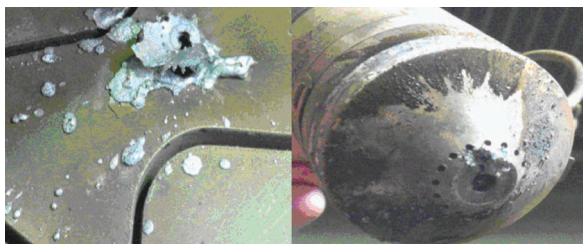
Застывший шлак, повторяющий форму защитного колпачка
